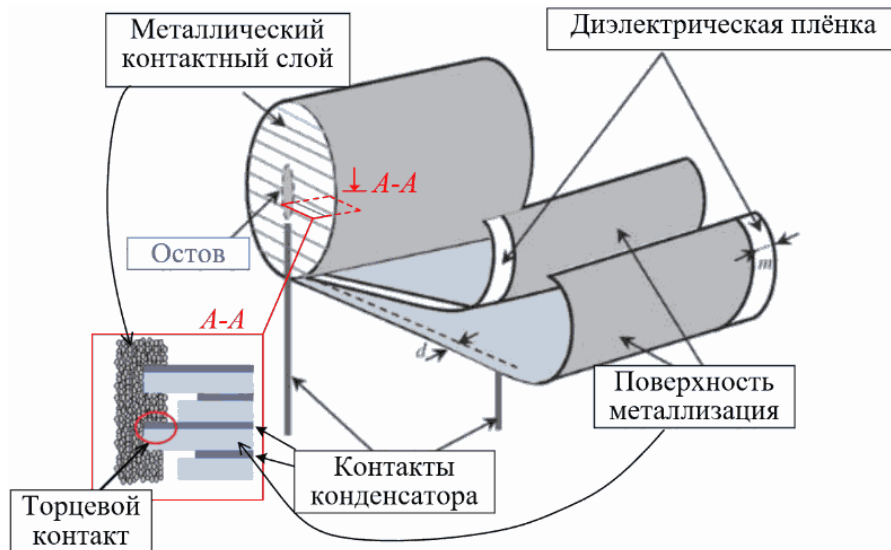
Конструкция металлопленочного конденсатора [137]
